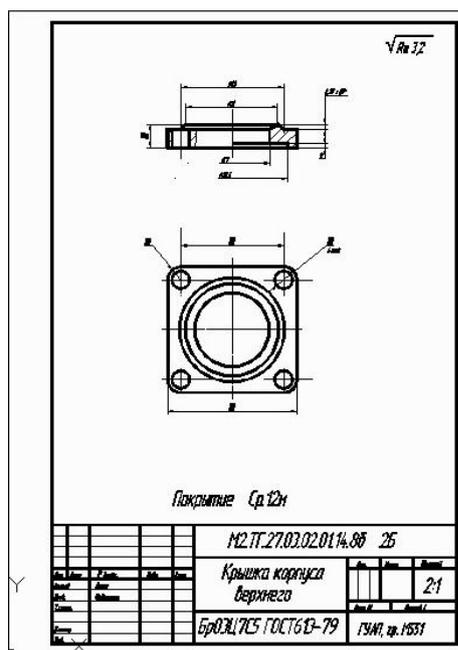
Электронная 2-D модель детали «Крышка корпуса верхнего».
